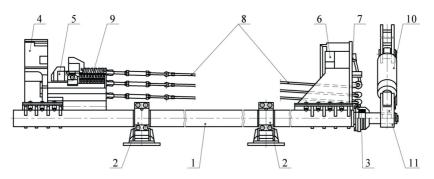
Сепаратор: 1 – стойка; 2 – подшипники скольжения; 3 – подшипники качения; 4 – кассета верхняя; 5 – отсекатель; 6 – кассета нижняя; 7 – педаль; 8 – трос-тяга; 9 – пружина; 10 – гидроцилиндр; 11 – рычаг
